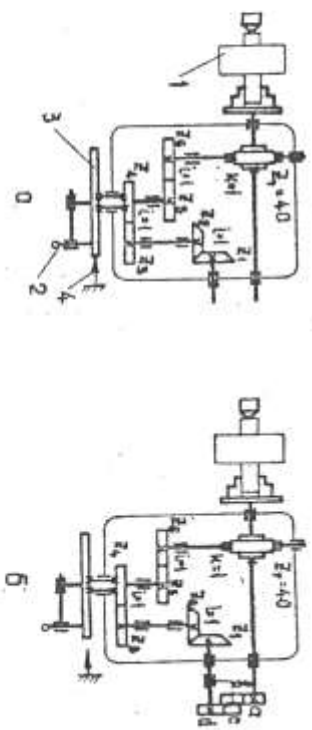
Кінематична схема універсальної дільничої головки настроєної на:
